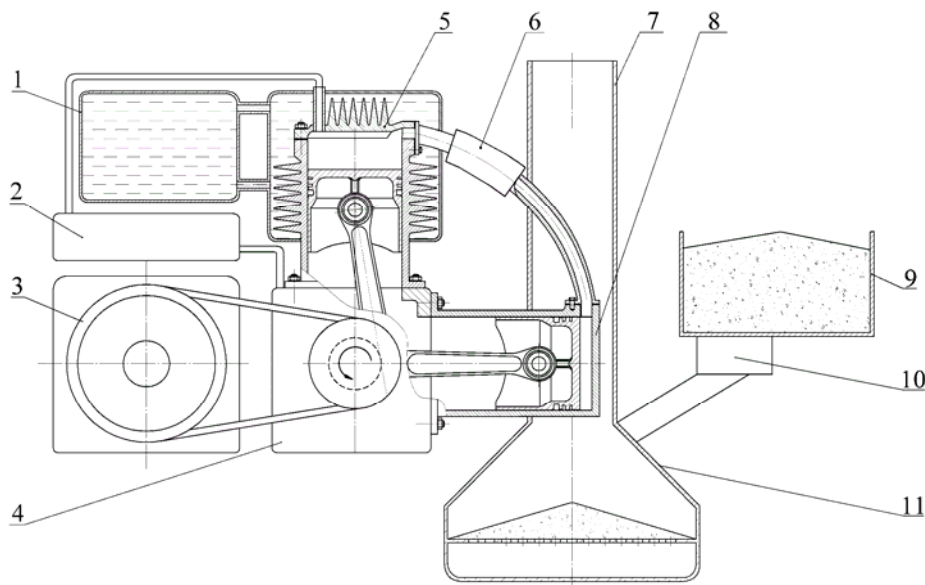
Принципова схема установки: 1 – радіатор; 2 – компресор повітряний; 3 – приводний механізм; 4 – двигун Стірлінга; 5 – холодний циліндр; 6 – регенератор; 7 – димова труба; 8 – гарячий циліндр; 9 – бак з паливом; 10 – пристрій дозування і подачі палива; 11 – топка
